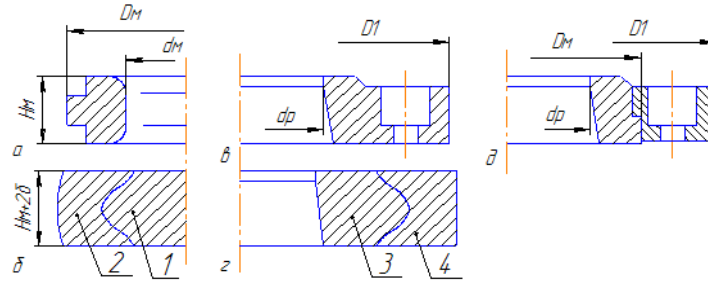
Вплив конструкції матриці на якість металу, з якого виготовляються її робочі елементи
